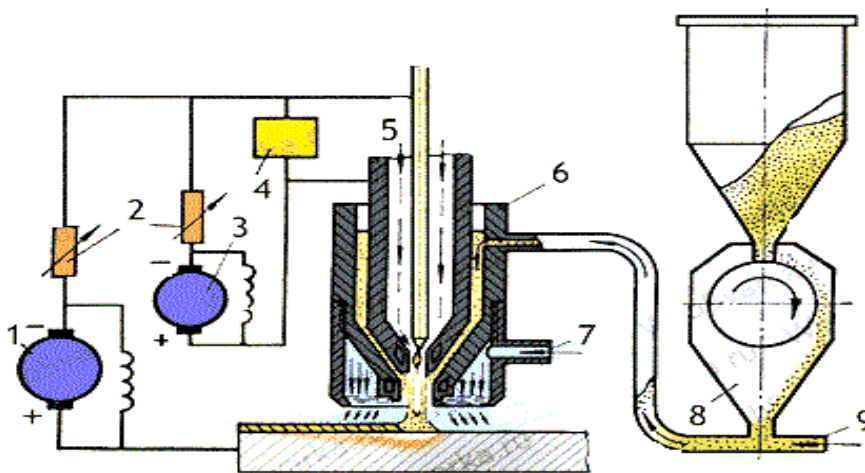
Схема установки для плазмового наплавлення металевим порошком: 1 – джерело живлення дуги прямої дії; 3 – джерело живлення дуги непрямої дії; 2 – опори баластні; 4 – осцилятор; 6 – корпус пальника; 5 – сопло для плазмоутворювального газу; 7 – отвір для входу захисного газу; 8 – живильник для подачі порошку; 9 – трубка, за допомогою якої подається газ, який несе порошок [5].
